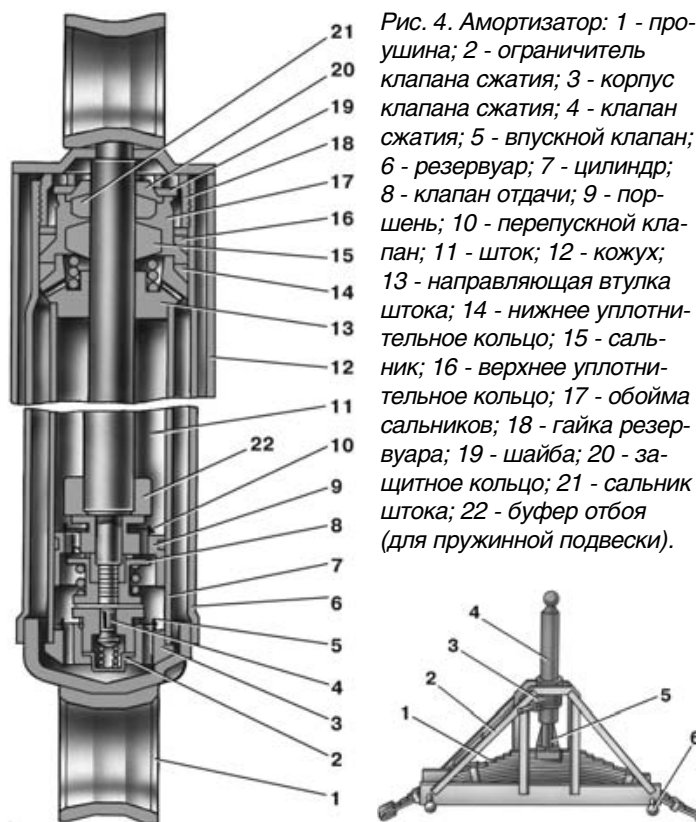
Амортизатор: 1 - проушина; 2 - ограничитель клапана сжатия; 3 - корпус клапана сжатия; 4 - клапан сжатия; 5 - впускной клапан; 6 - резервуар; 7 - цилиндр; 8 - клапан отдачи; 9 - поршень; 10 - перепускной клапан; 11 - шток; 12 - кожух; 13 - направляющая втулка штока; 14 - нижнее уплотнительное кольцо; 15 - сальник; 16 - верхнее уплотнительное кольцо; 17 - обойма сальников; 18 - гайка резервуара; 19 - шайба; 20 - защитное кольцо; 21 - сальник штока; 22 - буфер отбоя (для пружинной подвески).
